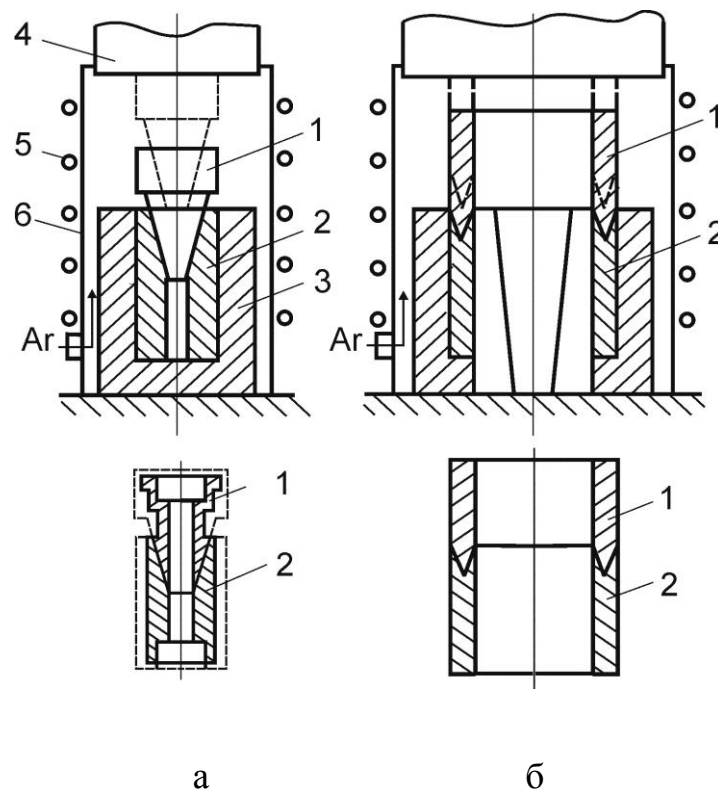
Технологических схемы клинопрессовой сварки трубчатых переходников малого (а) и большого (б) диаметра: 1 - заготовка из титанового сплава; 2 - заготовка из алюминиевого сплава; 3 - пресс-форма; 4 - шток пресса; 5 - нагреватель; 6 - корпус камеры
